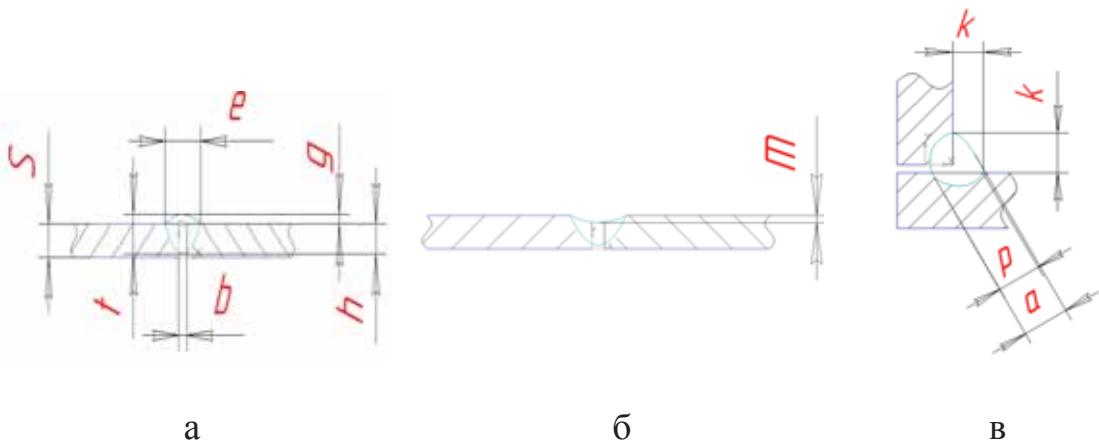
Основные геометрические параметры стыковых (а, б) и углового (в) сварных швов: S – толщина детали; e – ширина шва; g – выпуклость(усиление); h – вогнутость (ослабление); t – толщина стыкового шва; b – зазор в стыке; k – катет углового шва; p – расчетная высота углового шва; a – толщина углового шва
